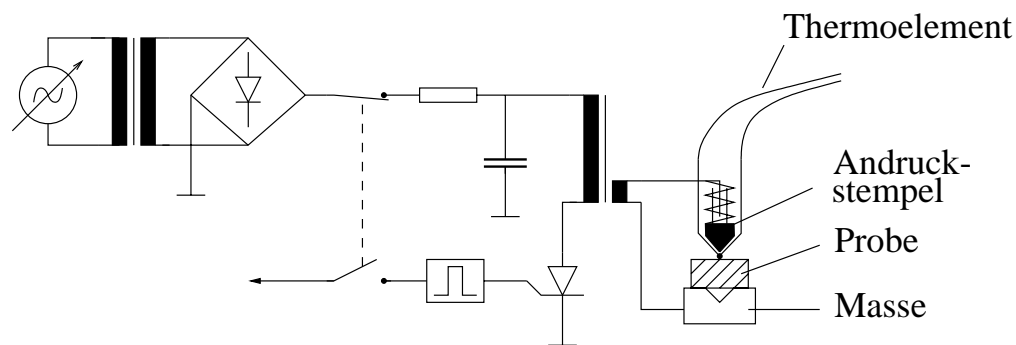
Prinzipskizze des Impulsstrom-Schweißgerätes
